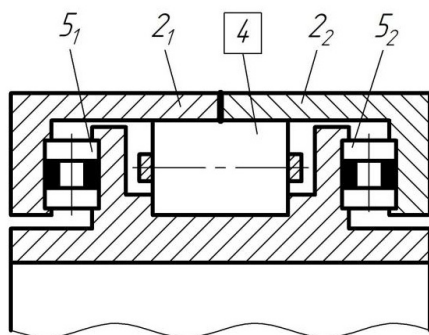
Роликовый радиально-упорный подшипник с телами качения, расположенными на одной линии
